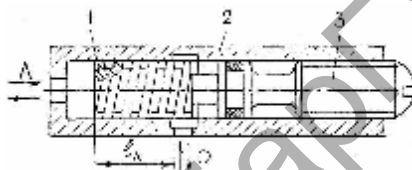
Винтовой (линейный) регулируемый дроссель:
